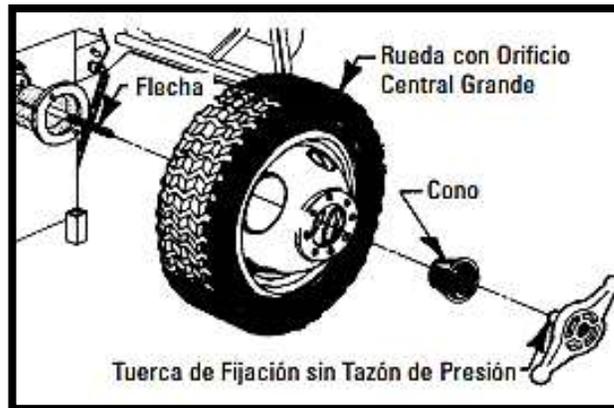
Montaje de neumático con cono delantero en máquina balanceadora
